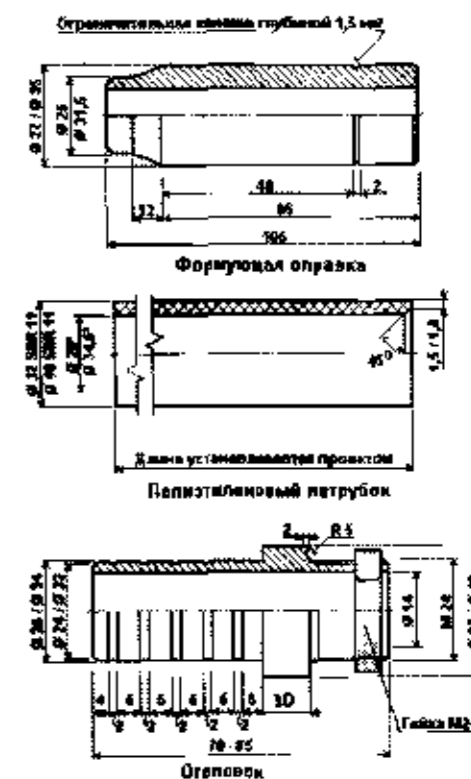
Детали для изготовления перехода «полиэтилен – металл»
